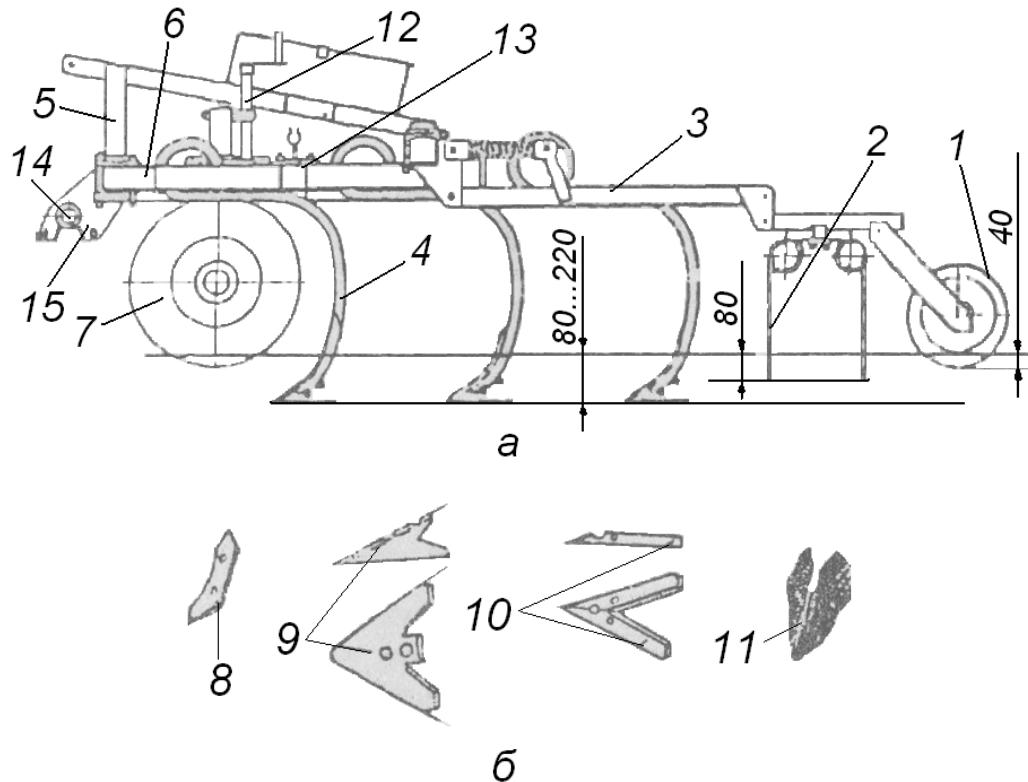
Агрегат чизельный универсальный АЧУ-2,8:
